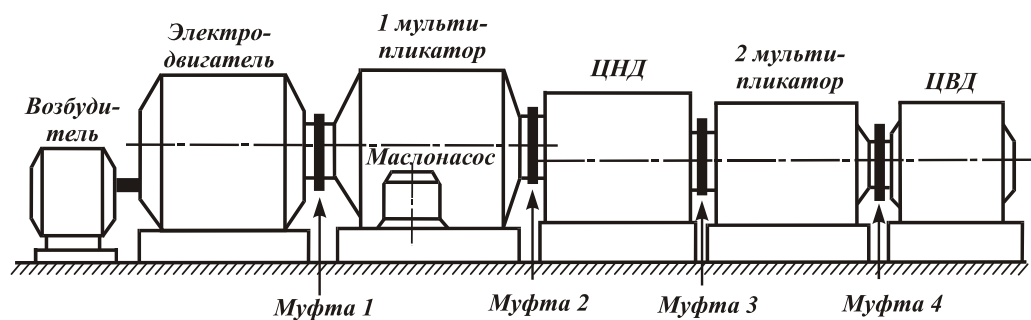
Компоновочная схема компрессора К-380-103-1
